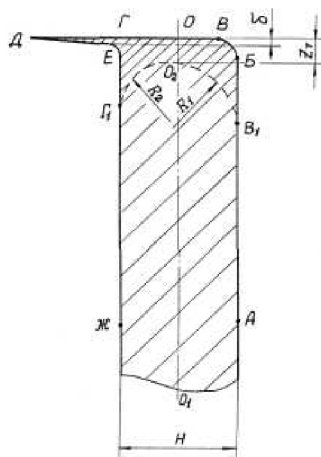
Конфигурация кромки заготовки: δ - дефектный слой, z_1 - минимальный торцевой припуск
